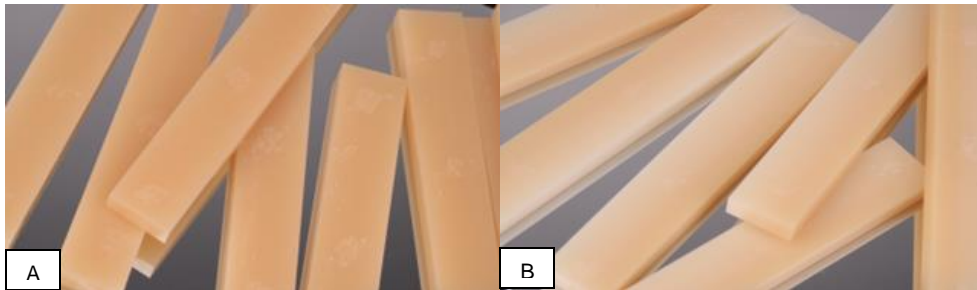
Barras fresadas mediante tecnología CAD/CAM (A) Disco G-CAM (B) Disco CERAMILL
